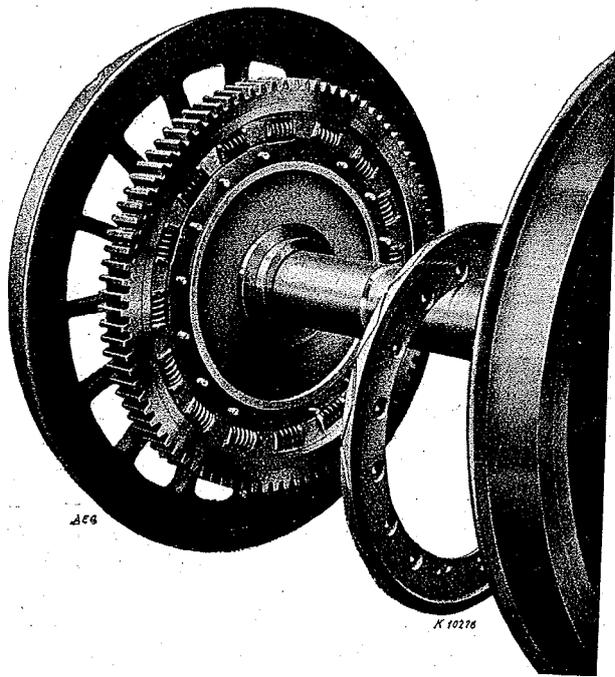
I Co+Co I Lokomotive, Gefederter Zahnkranz.
